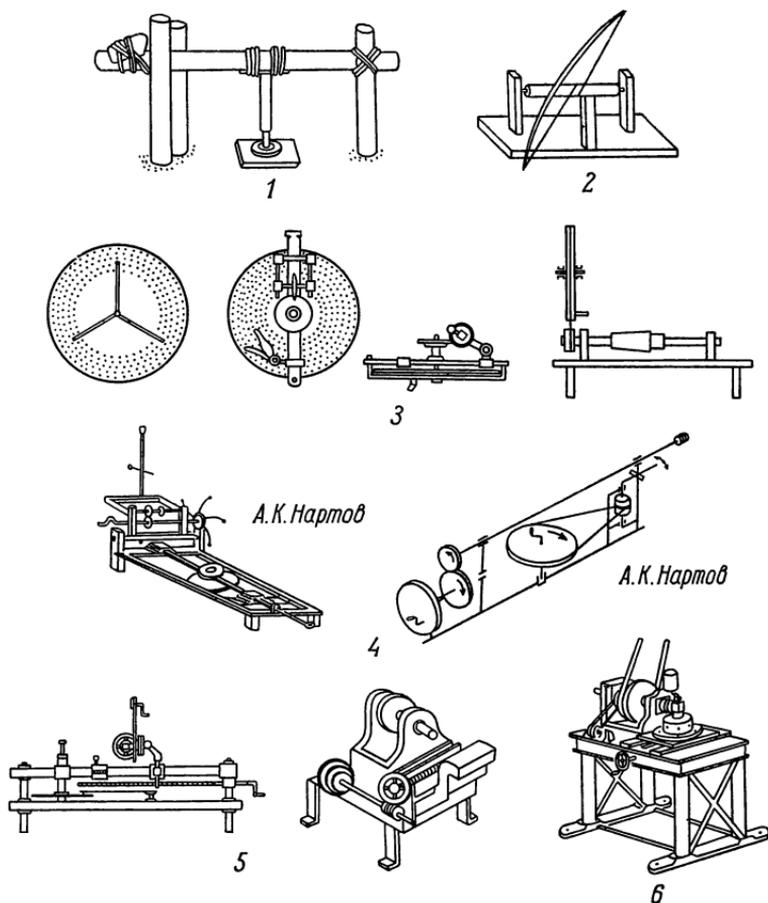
Развитие конструкций фрезерных станков. Публикуется впервые.
